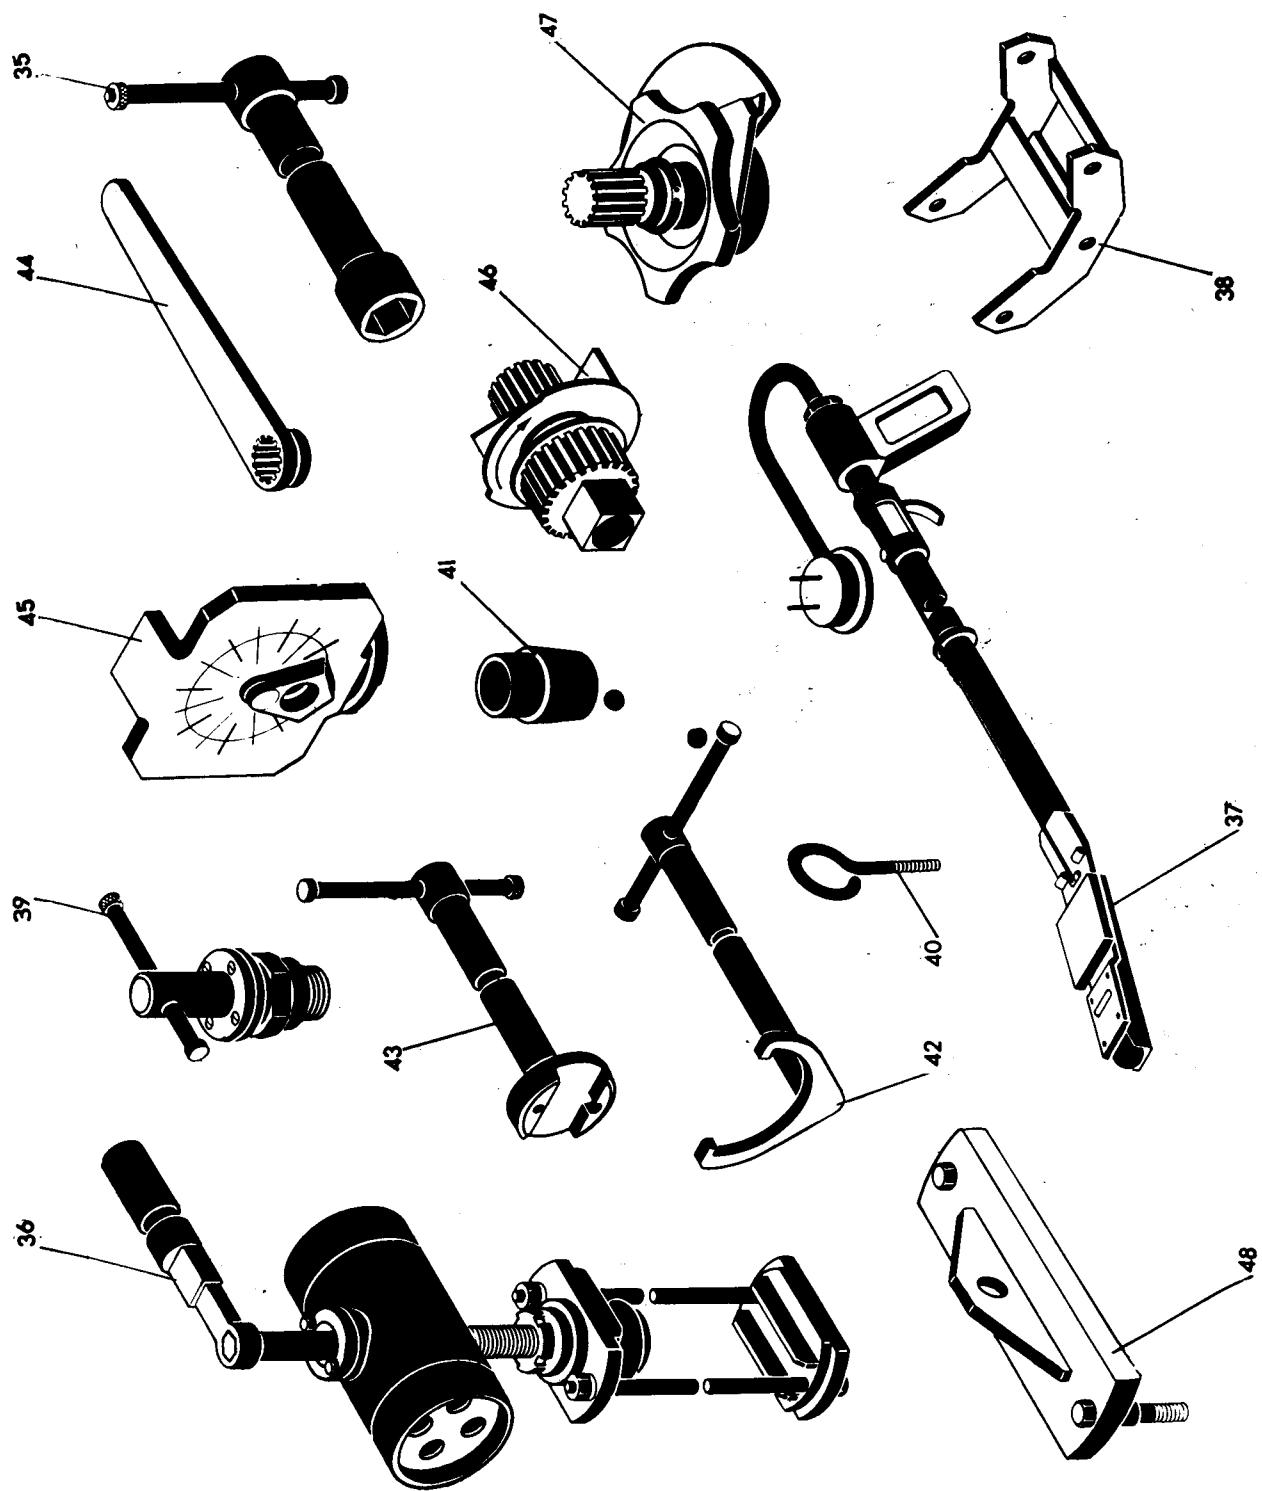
Втулка рабочего цилиндра. Приспособления
